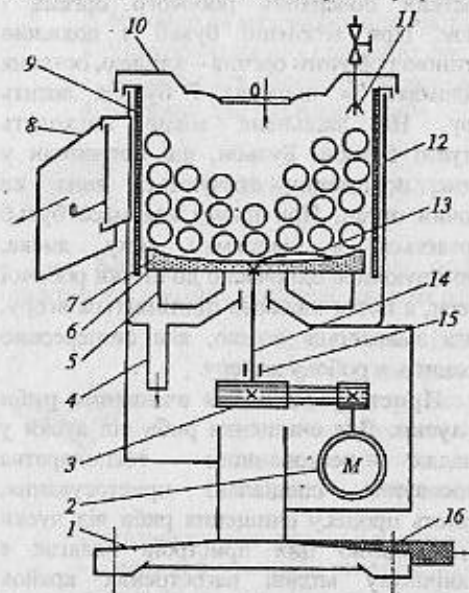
Принципова схема картоплеочищувальної машини МОК-150: 1 – станина; 2 – електродвигун; 3 – знижуюча клиноремінна передача; 4 – зливний патрубок; 5 – лопаті; 6 – металевий диск; 7 – абразивний диск; 8 – розвантажувальний лоток; 9 – металевий циліндр з отворами; 10 – завантажувальний лоток; 11 – ніпель; 12 – робоча камера; 13 – хвиля; 14 – вертикальний вал; 15 – підшипник; 16 – зливний шланг
